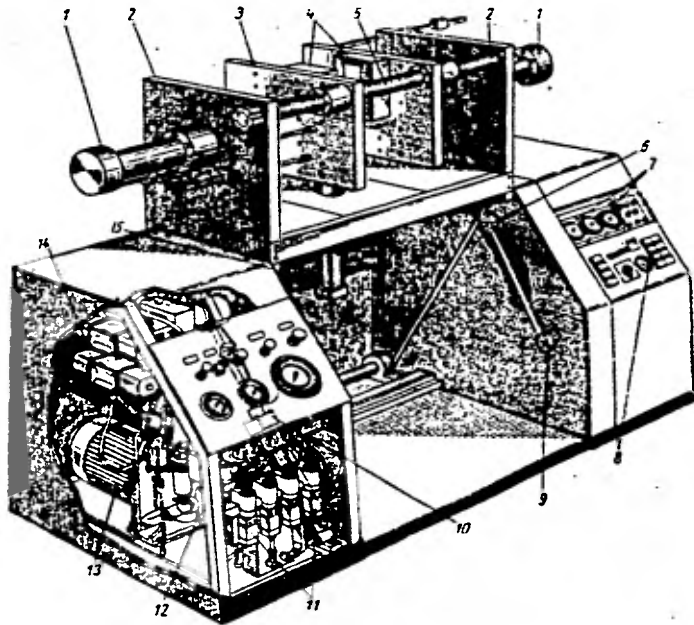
MAQUINA DE MOLDEO POR SOPLADO.
